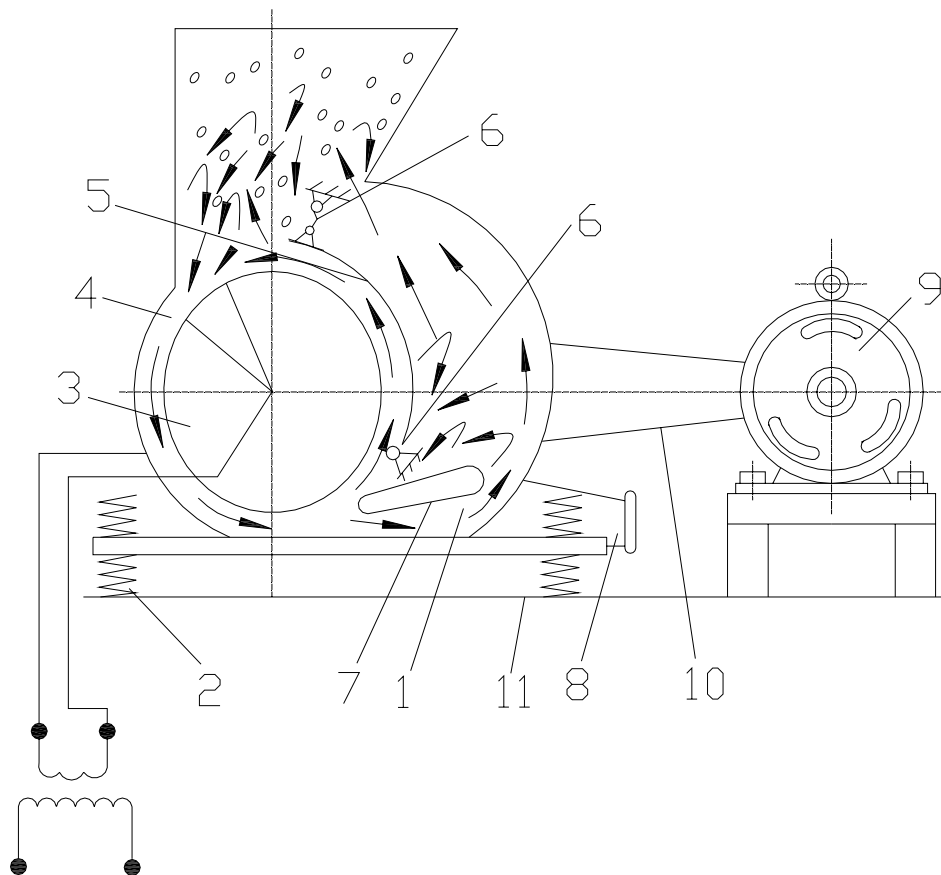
Вертикальный вибросмеситель: 1 – корпус; 2 – упругие опоры; 3 – ротор; 4 – дебаланс; 5 – откидной щиток; 6 – шарниры; 7 – рассекатель; 8 – разгрузочное устройство; 9 – электродвигатель; 10 – клиноремённая передача; 11 – станина
